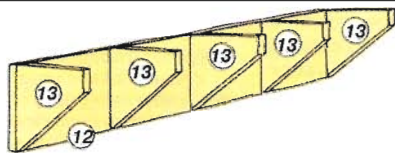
Настенный держатель состоит из доски и прикрепленных к ней перегородок между отделениями для лыж. Перегородки крепят к доске на шкантах с клеем.
